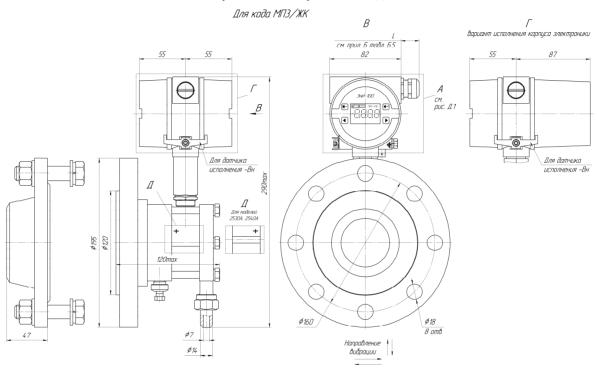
Датчики специального фланцевого конструктивного исполнения моделей 2530, 2540, 2530A, 2540A. Соединение и развальцовка трубопровода Ø7 по ГОСТ 13954-74. Фланец присоединительный для установки датчика на стенке резервуара по ГОСТ 12815-80 исп. 3 (ряд 1), PN = 4,0 МПа, DN = 80 мм. В комплекте с фланцем паронитовая прокладка Б-80-100 ПОН по ГОСТ 15180-86
